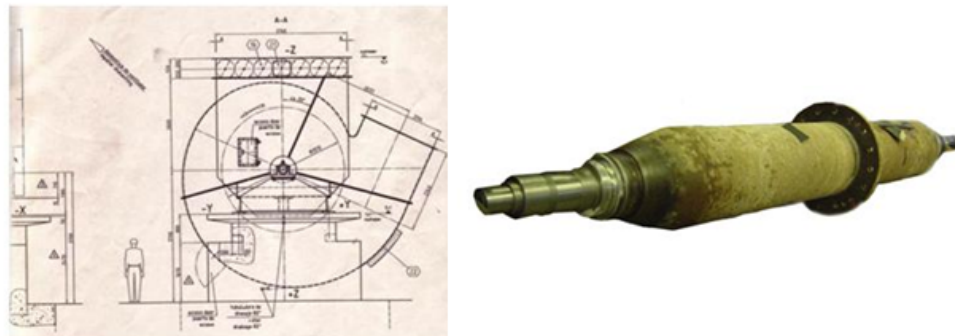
Vista general del ventilador con sus dimensiones exteriores y vista del árbol.
